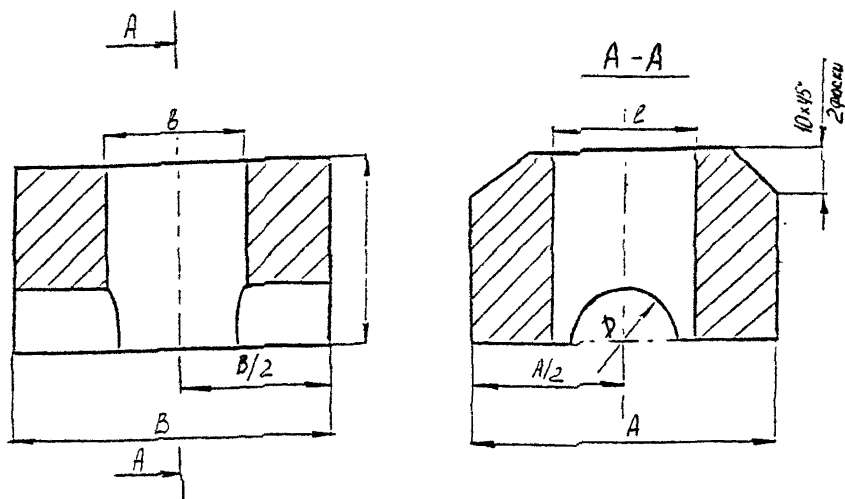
Конструкция инвентарной медной формующей детали для комбинированной сварки стыковых соединений стержней в горизонтальном положении
